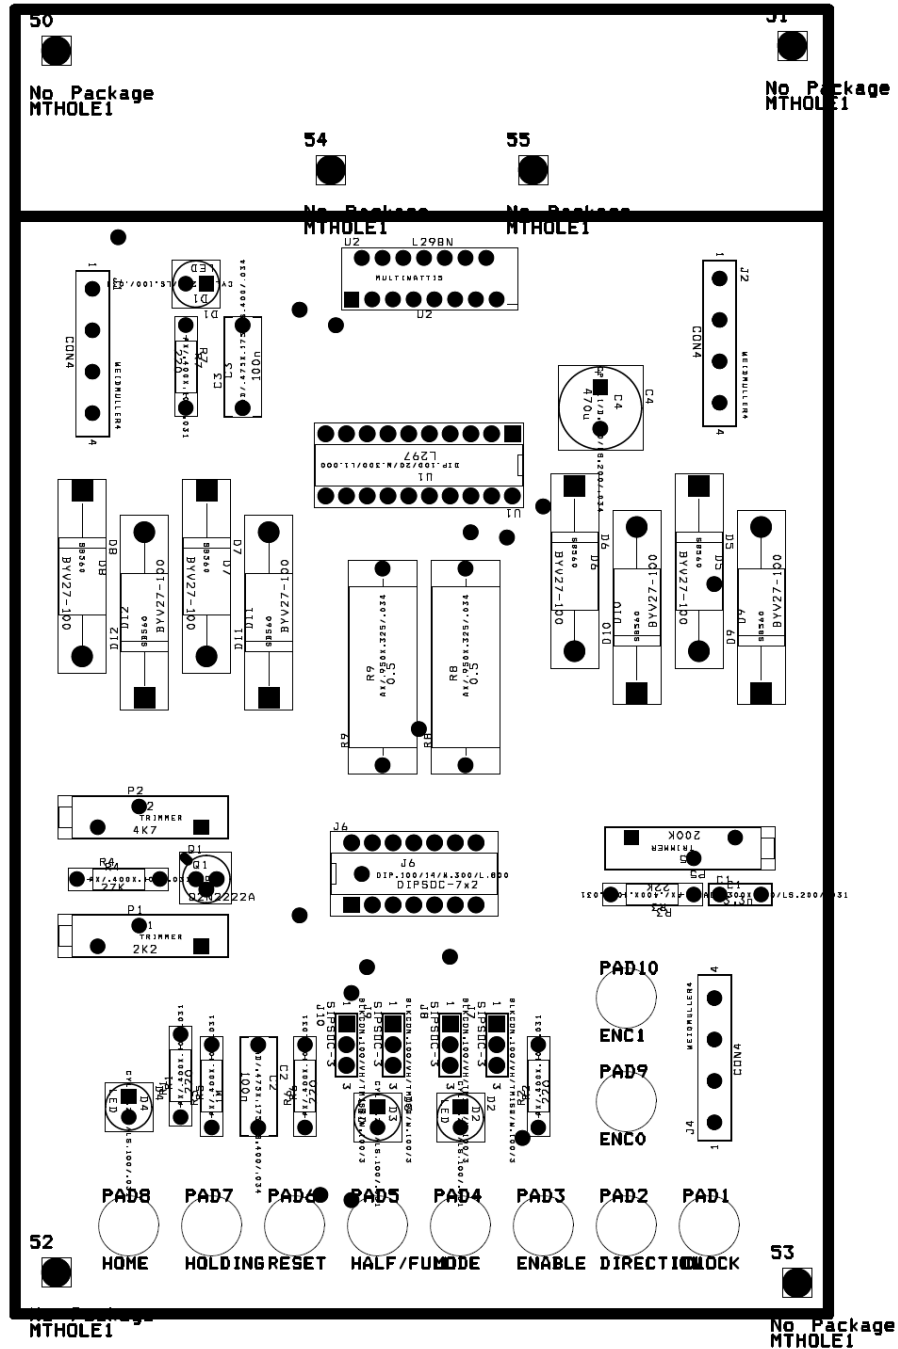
Capa d'acoblament (AST) de la PCB de la interfície per al motor bipolar
